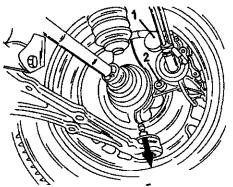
Отжать поперечный рычаг вниз по направлению стрелки до освобождения пальца шаровой опоры. Болтами (1) и (2) крепится тормозной суппорт.
